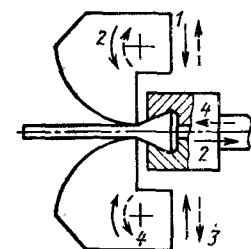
Схема холодного вальцевания пера рабочей лопатки компрессора:
